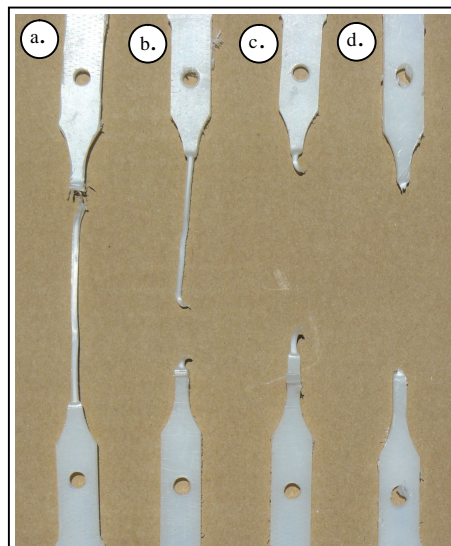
Foto de las probetas ensayadas con los distintos modos de falla: a) Falla en soldadura con formación de cuello. b) Falla fuera de la zona de soldadura con acuellamiento. c) Falla fuera de la zona de soldadura con poco acuellamiento. d) Falla en soldadura sin formación de cuello.
